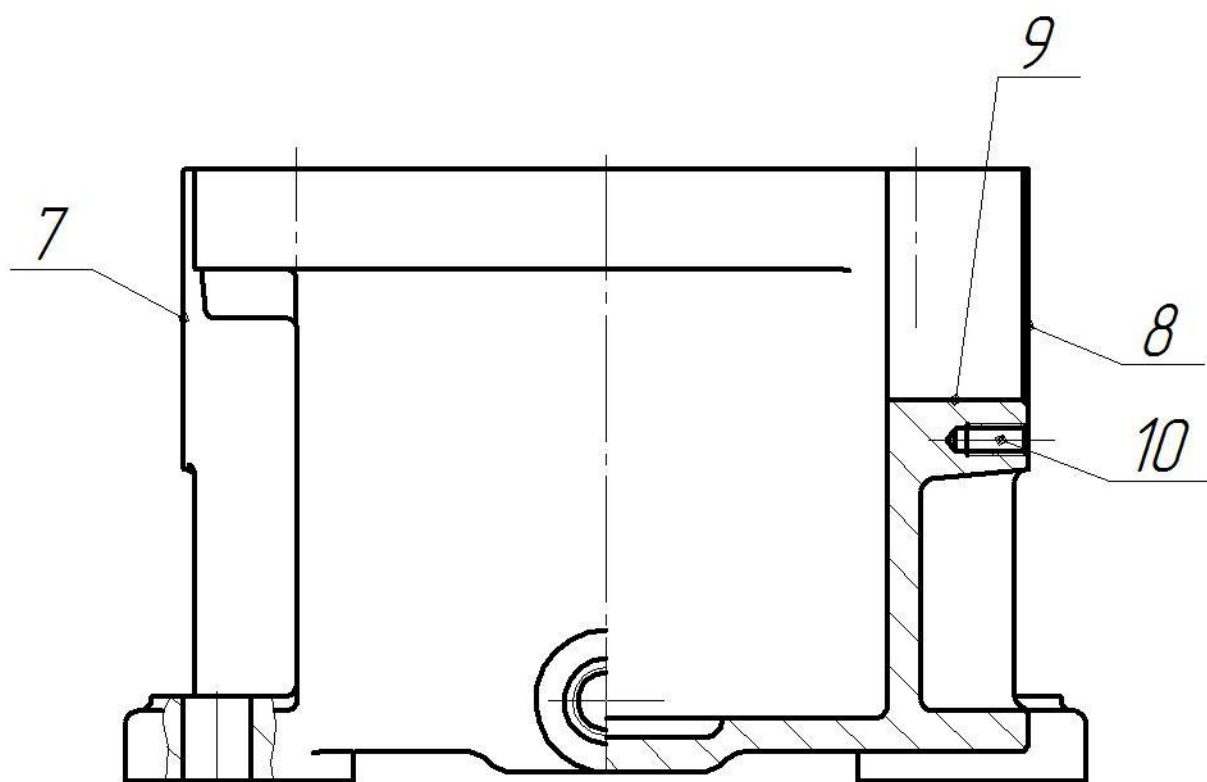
Вид сбоку корпуса червячного редуктора
